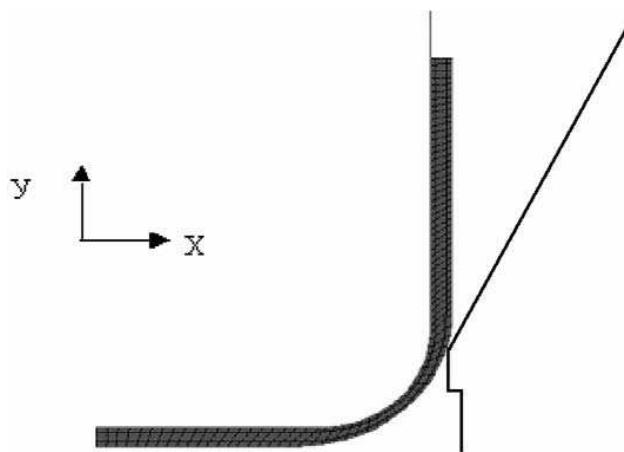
Кінцево-елементна модель процесу витягування двошарової заготовки
